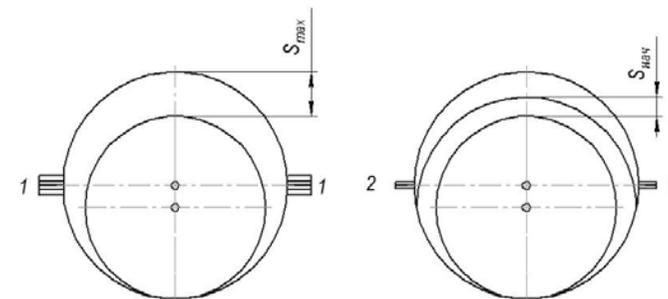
Регулировка зазора в подшипниках прокладками:
